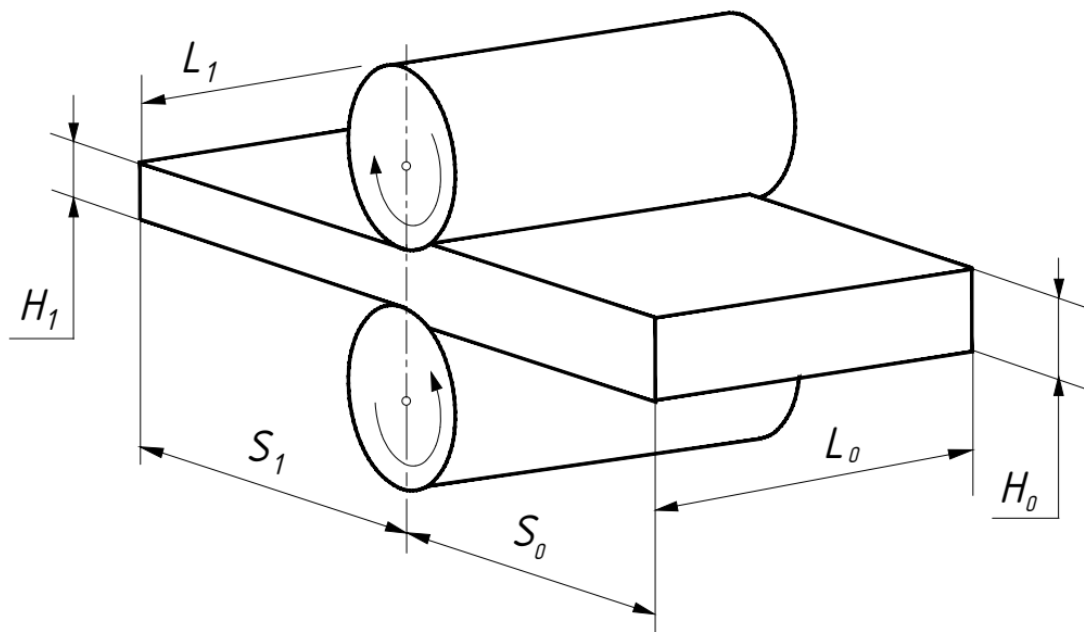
Схема прокатки прямолінійної смуги прямокутного поперечного перерізу між циліндричними валками
